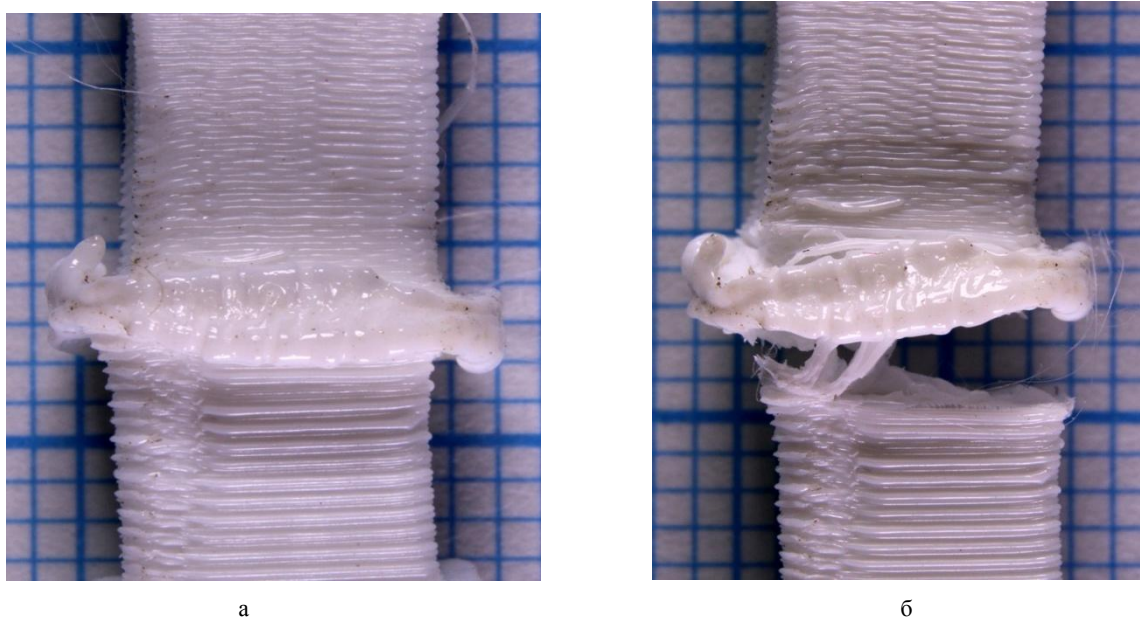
Стиковий зварний шов зразків з ПЛА: а — до; б — після механічного випробувань на розтяг
